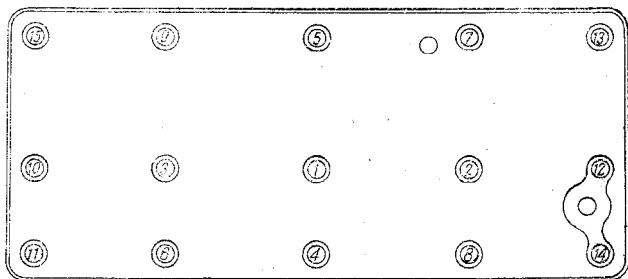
Последовательность затяжки гаек крепления головки цилиндров
